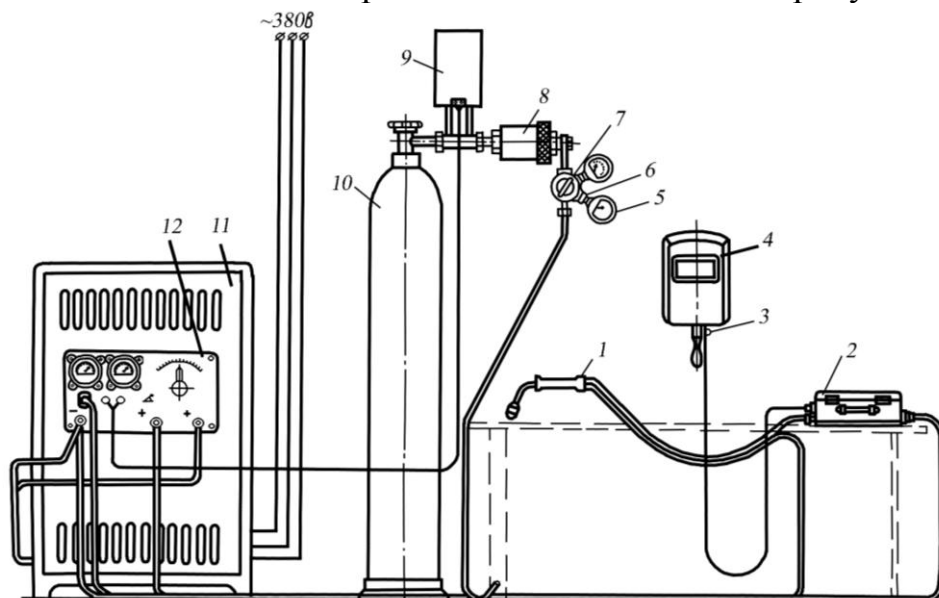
Схема механизированной сварки в углекислом газе:
